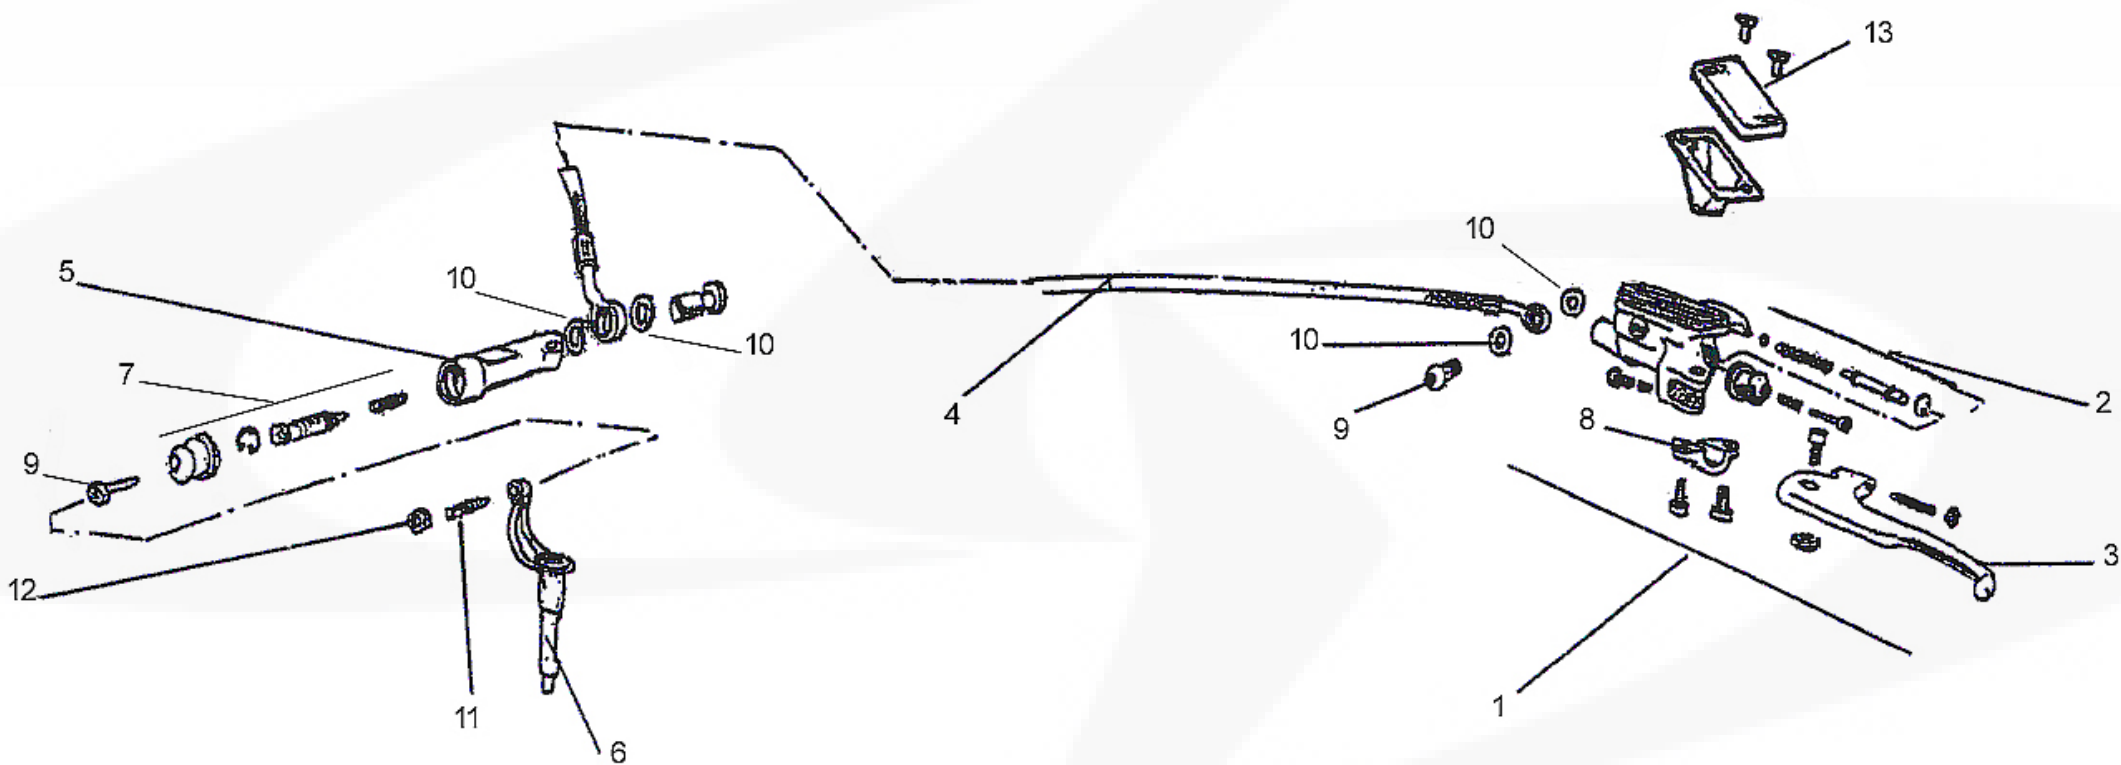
LEVIER D'EMBRAYAGE / CLUTCH LEVER / MANETA DE EMBRAGUE
